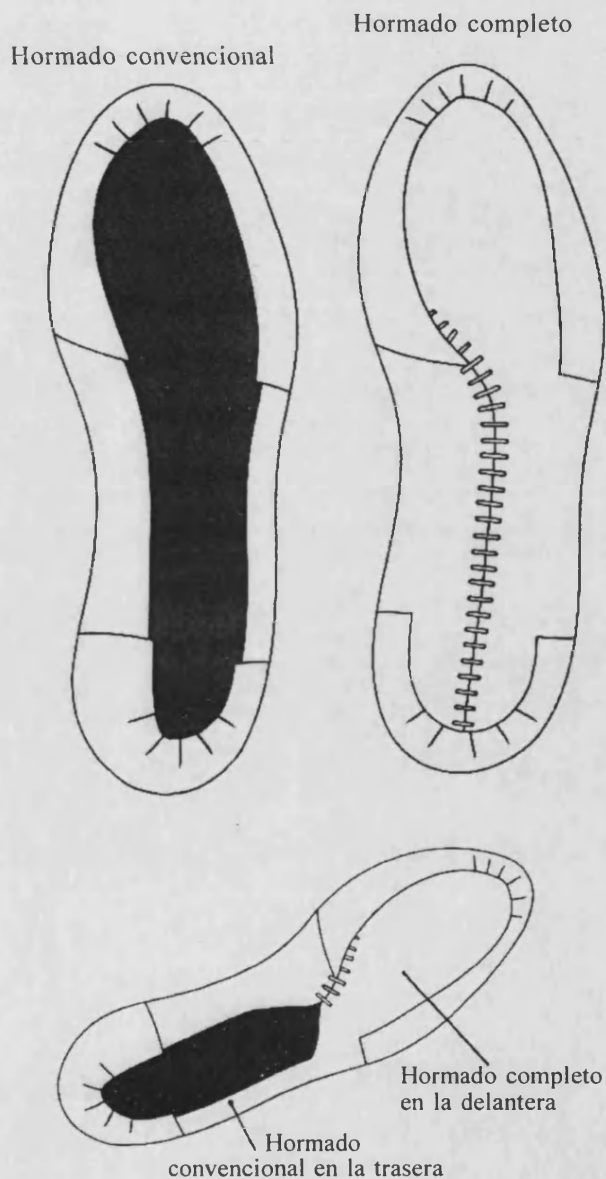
Vista superior del piso del calzado (sin plantilla) tras fijar el material de corte. Arriba a la izquierda hormado convencional, arriba a la derecha hormado completo y abajo hormado mixto (Ramiro y cols., 1989).
